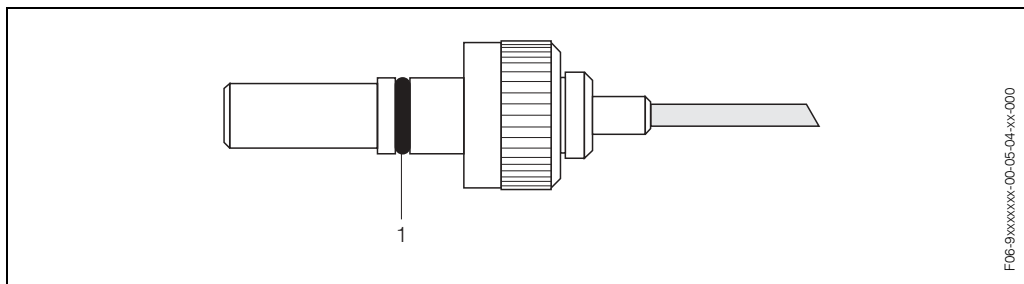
Монтаж кабельного ввода датчика для степени защиты IP 68
